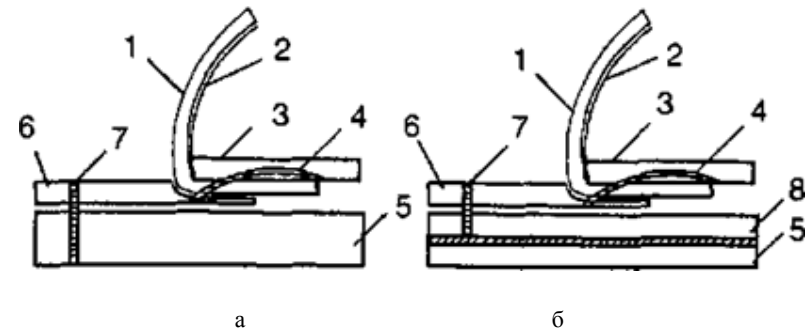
Схемы крепления деталей низа рантовой и рантово-клеевой обуви ручного производства: а – крепление деталей низа в рантовой обуви; б – крепление деталей низа в рантово-клеевой обуви: 1 – верх; 2 – подкладка; 3 – стелька; 4 – ниточный шов; 5 – подошва; 6 – рант; 7 – конец нитки; 8 – подложка (внутренняя подошва)
